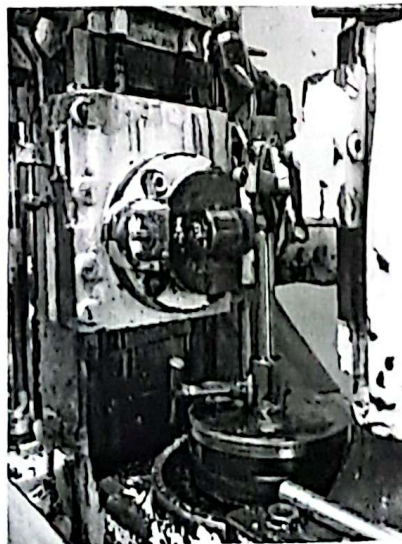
Mesin Bench Lathe melalui proses drill
